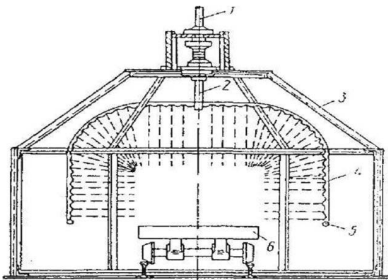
Однокамерна установка для очищення: 1 – підвідний патрубок; 2 – приєднувальний штуцер; 4 – перфорована труба; 5 – насадка; 6 – візок
